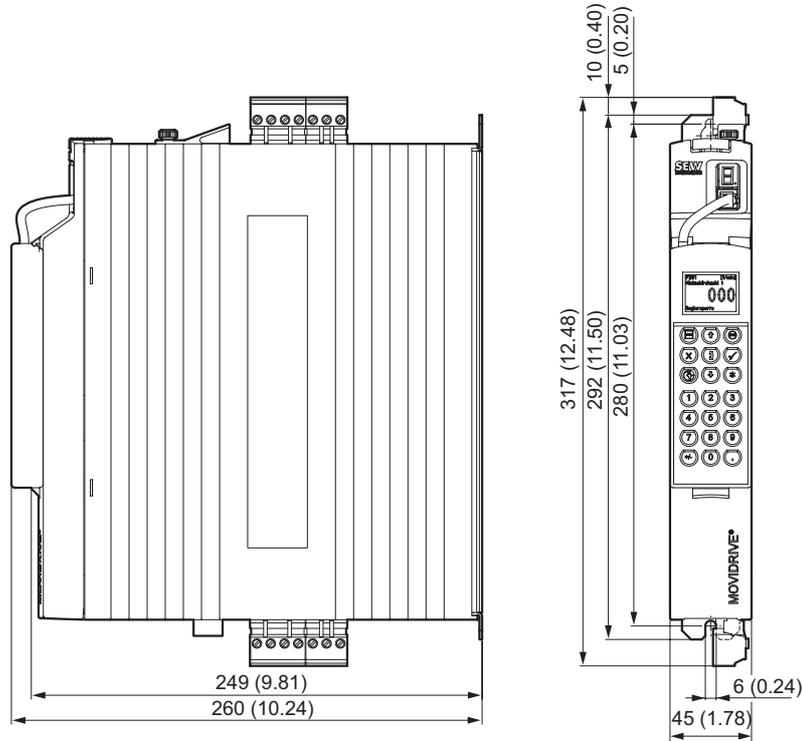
MDX60B 尺寸图, 规格 0S, 尺寸为 mm (in)
